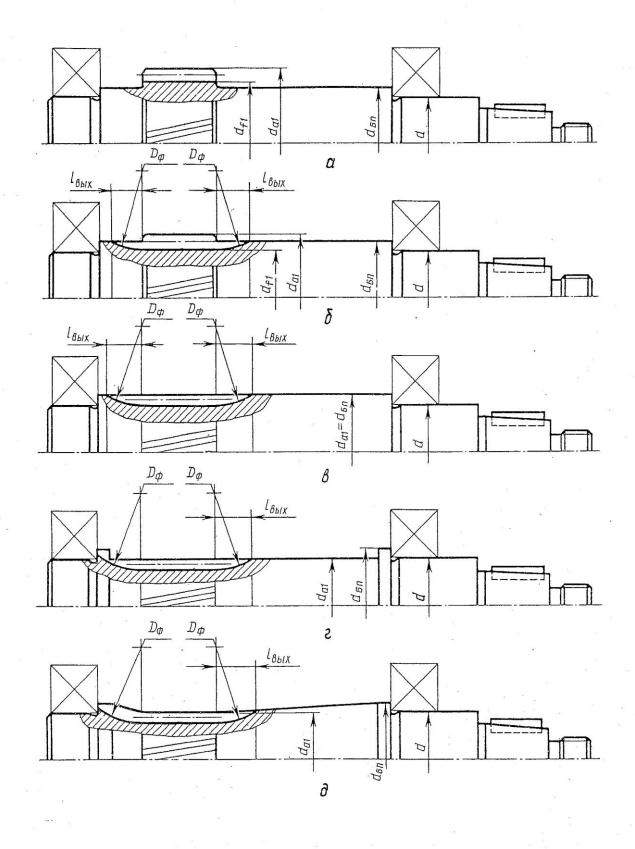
Конструкции быстроходных валов, выполненных за одно целое с цилиндрической зубчатой шестерней [2]
